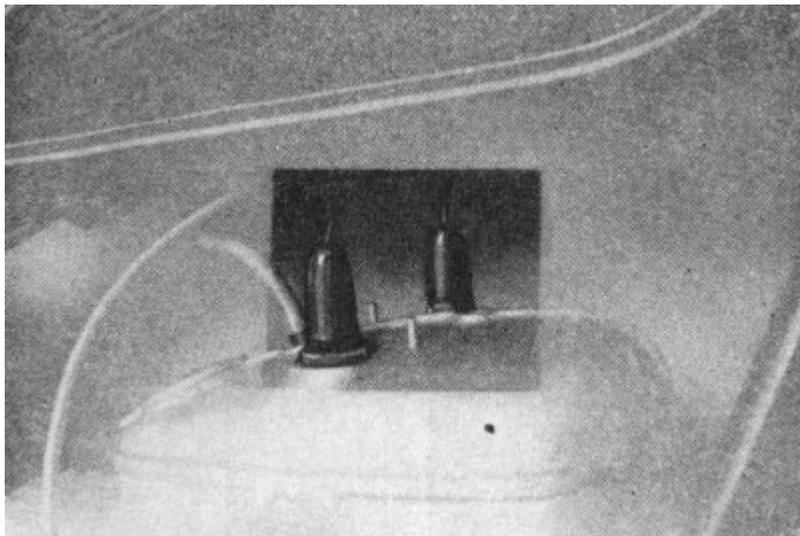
Gummischutzhauben für die Bowdenzugaufnahmen
